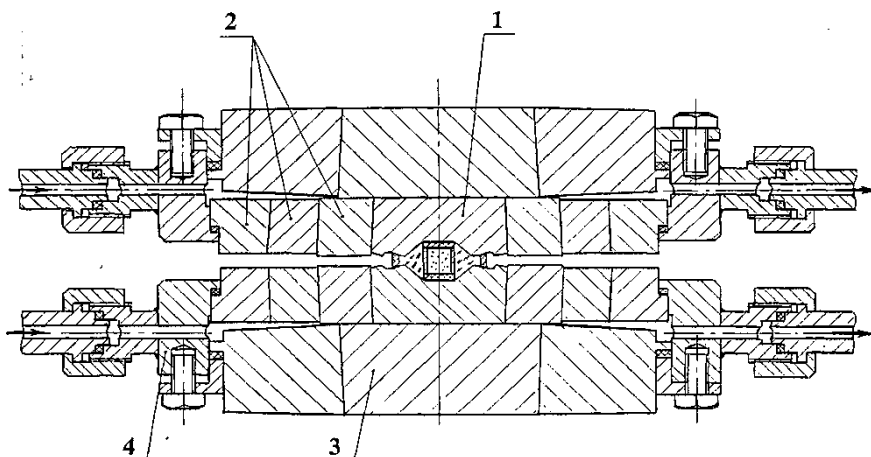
Устройство высокого давления для синтеза сверхтвердых материалов; 1 – твердосплавные матрицы с контейнером и нагревательным элементом; 2 – стальные поддерживающие кольца; 3 – твердосплавные опорные плиты с поддерживающими кольцами; 4 – корпус водяного охлаждения (стрелками указано направление входа и выхода воды)
